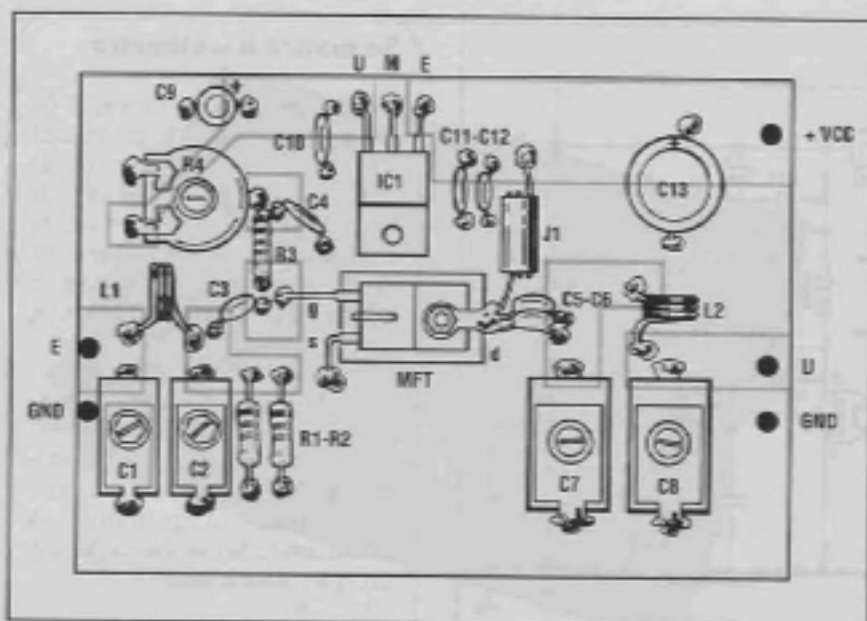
Disposizione pratica dei componenti: il montaggio è eseguito saldandoli direttamente sul lato rame.
